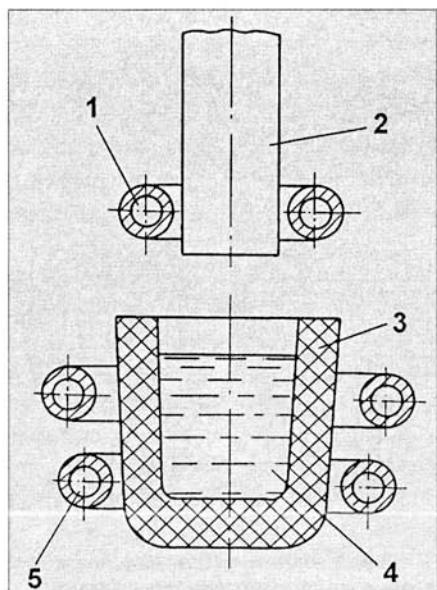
Наплавка подогретой детали погружением в форму—тигель с расплавленным сплавом
